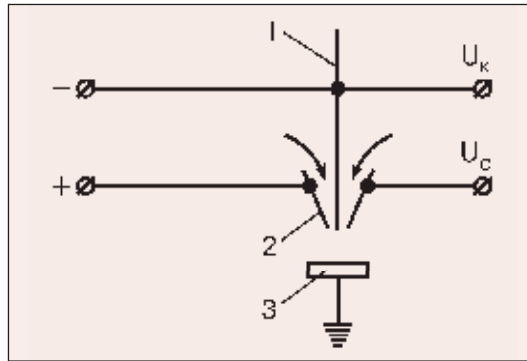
Схема способа микроплазменной сварки разнополярным током
